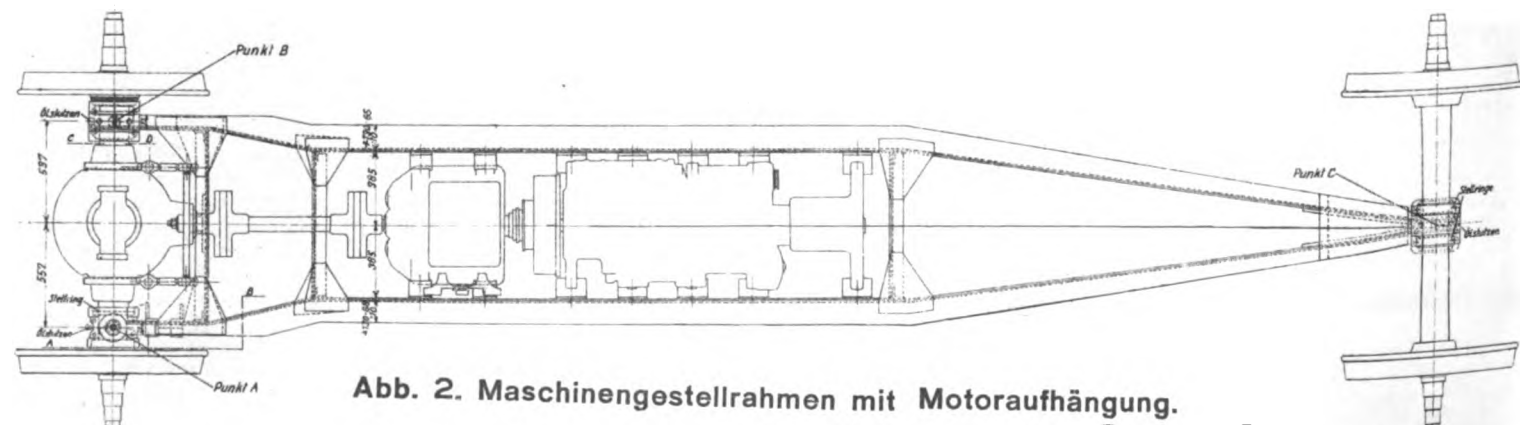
Maschinengestellrahmen mit Motoraufhängung.
